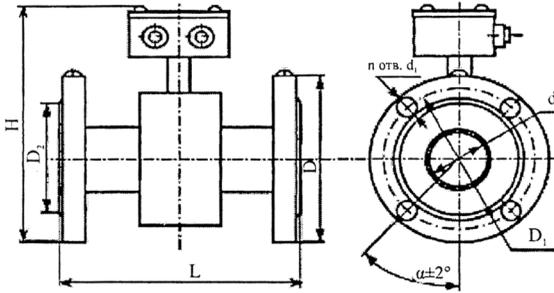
Габаритные и установочные размеры ПРПЭ типа ПРЭ 01
